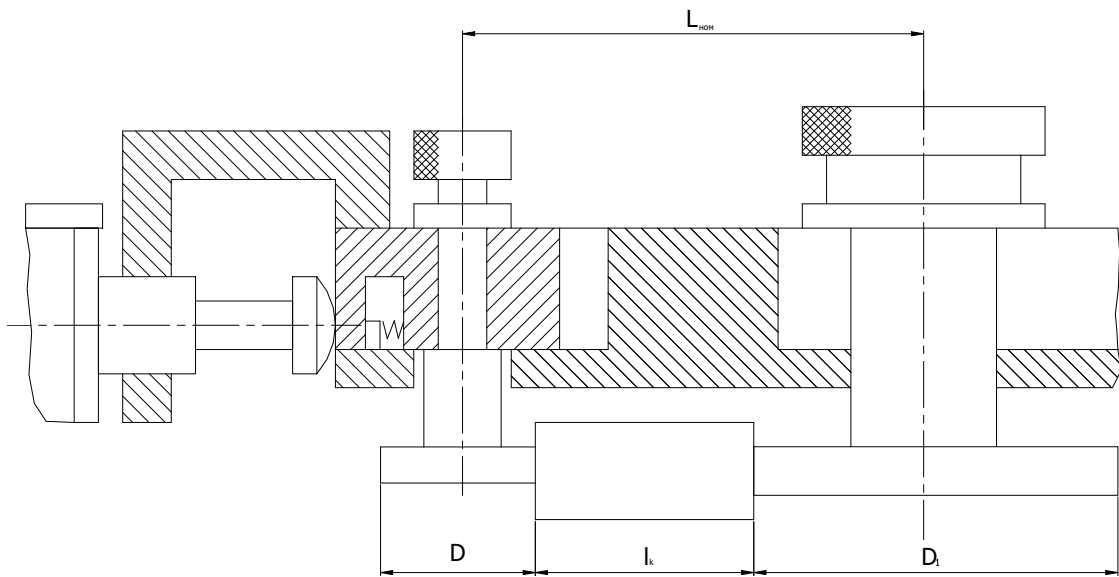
Схема налагоджування вимірювального пристрою на розмір
